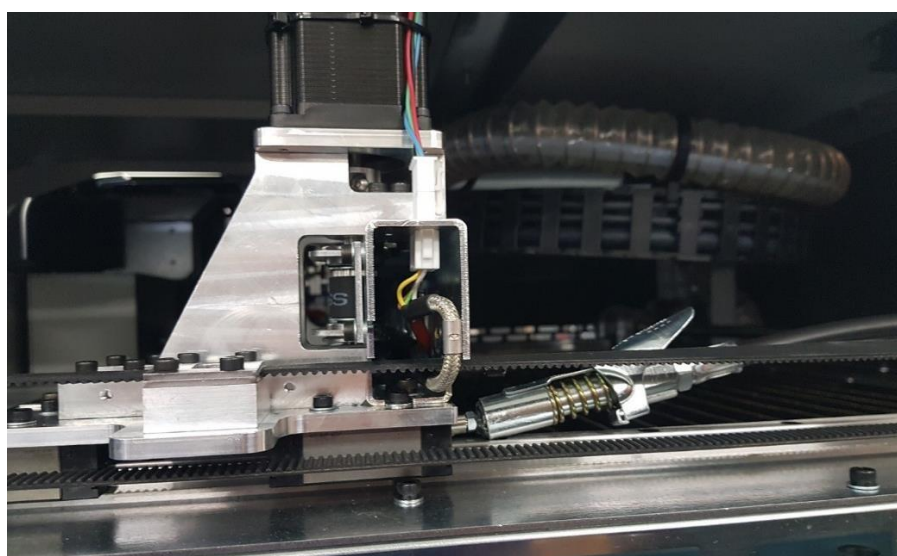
Подача смазки в смазочные ниппели в правой части принтера
